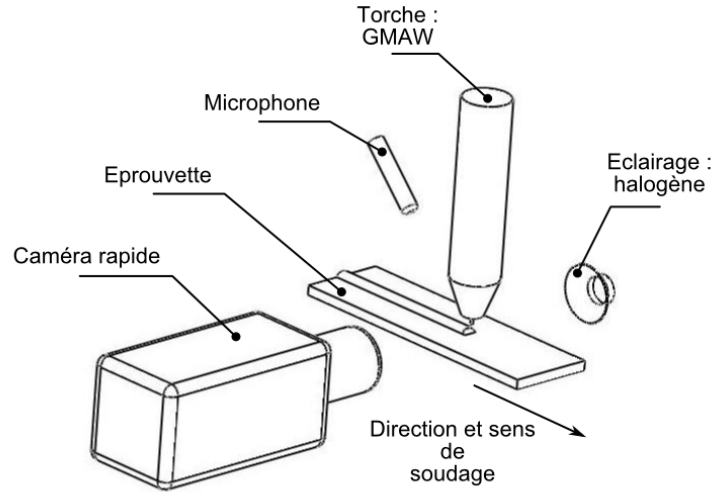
Dispositif expérimental pour la mesure acoustique en cours de soudage
